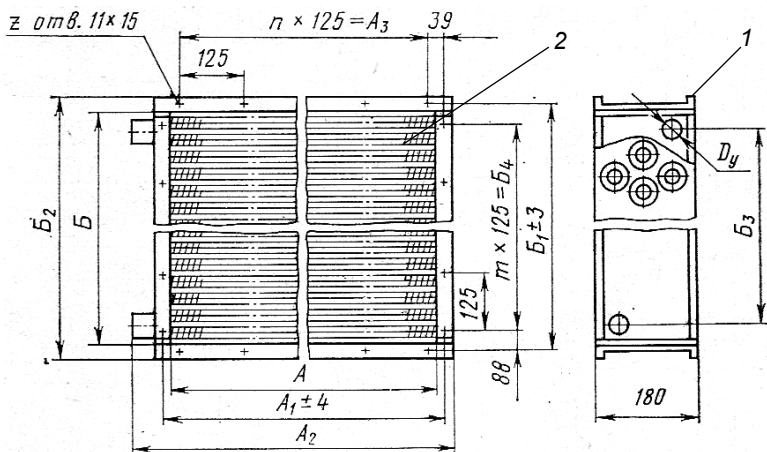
Схема калорифера: 1 – корпус; 2 – труба нагревателя
